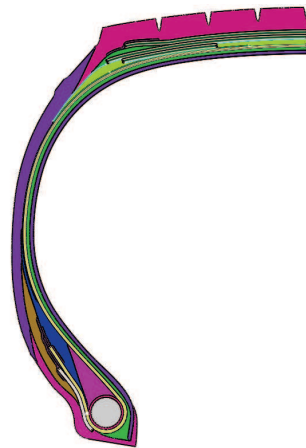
Exemple d’une coupe 2D du pneumatique à industrialiser.
